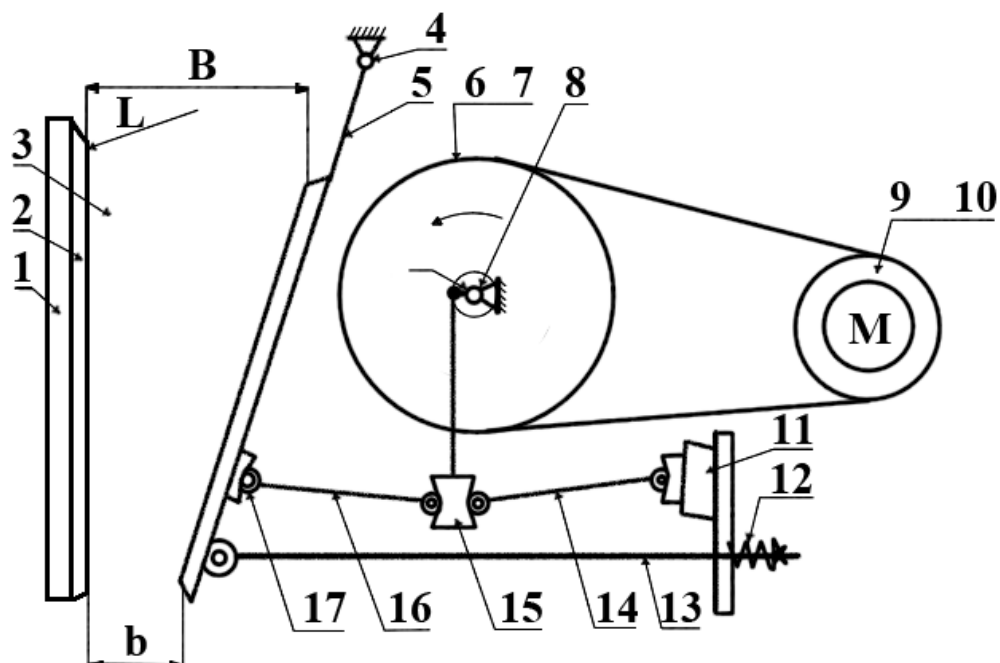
Кинематическая схема щековой дробилки с простым движением щеки: 1 – неподвижная щека; 2 – дробящая плита; 3 – боковая стенка; 4 – ось подвески подвижной щеки; 5 – подвижная щека; 6 – шкив; 7 – маховик; 8 – эксцентриковый вал; 9 – ведущий шкив; 10 – электродвигатель; 11 - регулировочное устройство; 12,13 – пружина и тяга замыкающего устройства; 14,16–распорные плиты; 15–шатун; 17 – опоры качения
